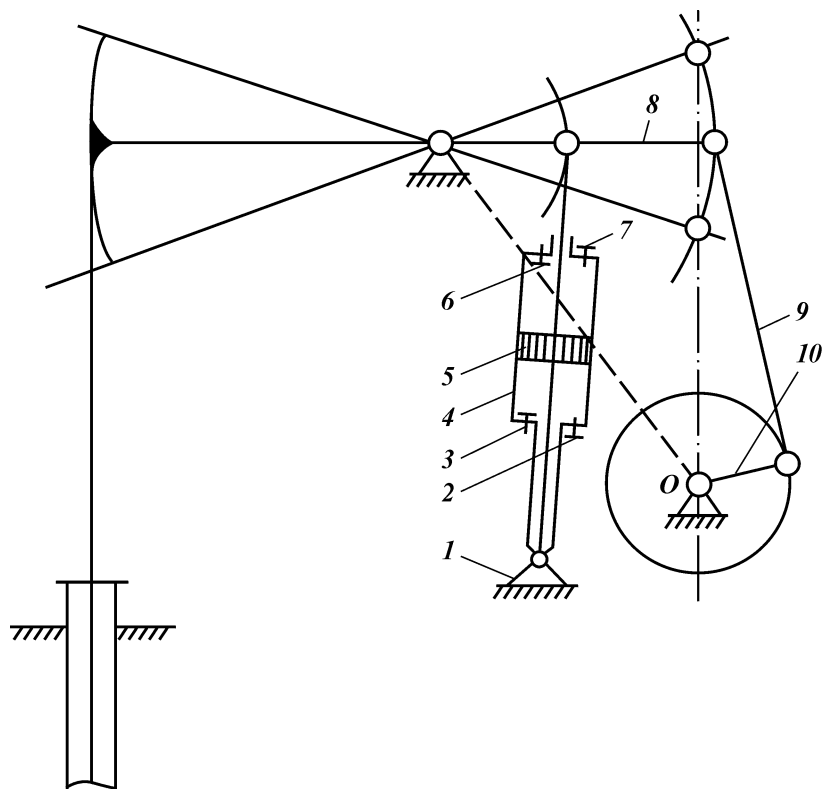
Кинематическая схема станка-качалки с подвесным компрессором:
